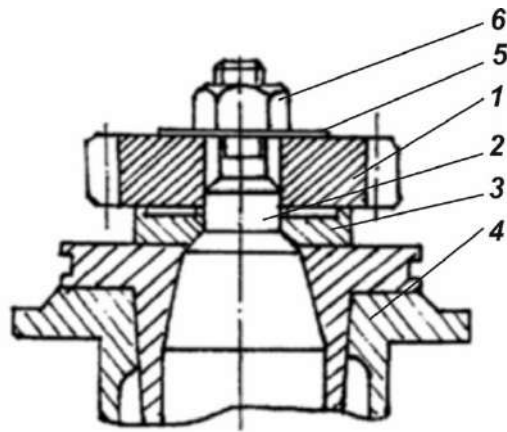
Схема закріплення заготовки гайкою у пристрої зубофрезерного верстата
